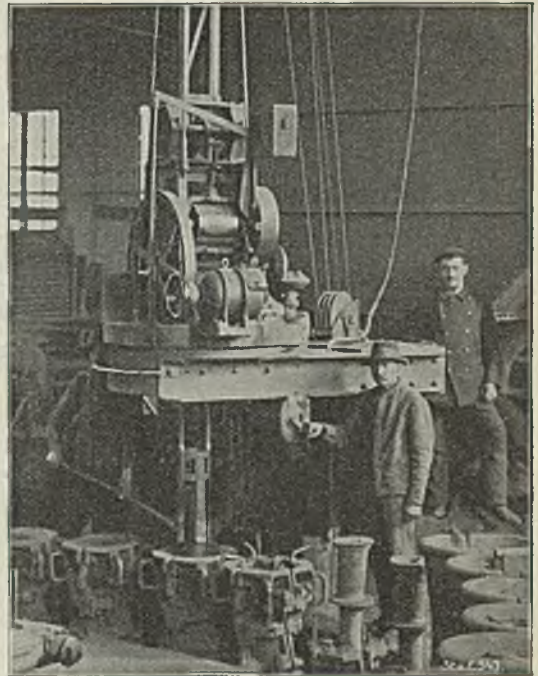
Ardelt's Rohrformstempelmaschine mit Freifallstampfer, Formen für Flanschenrohre aufstempelnd.
